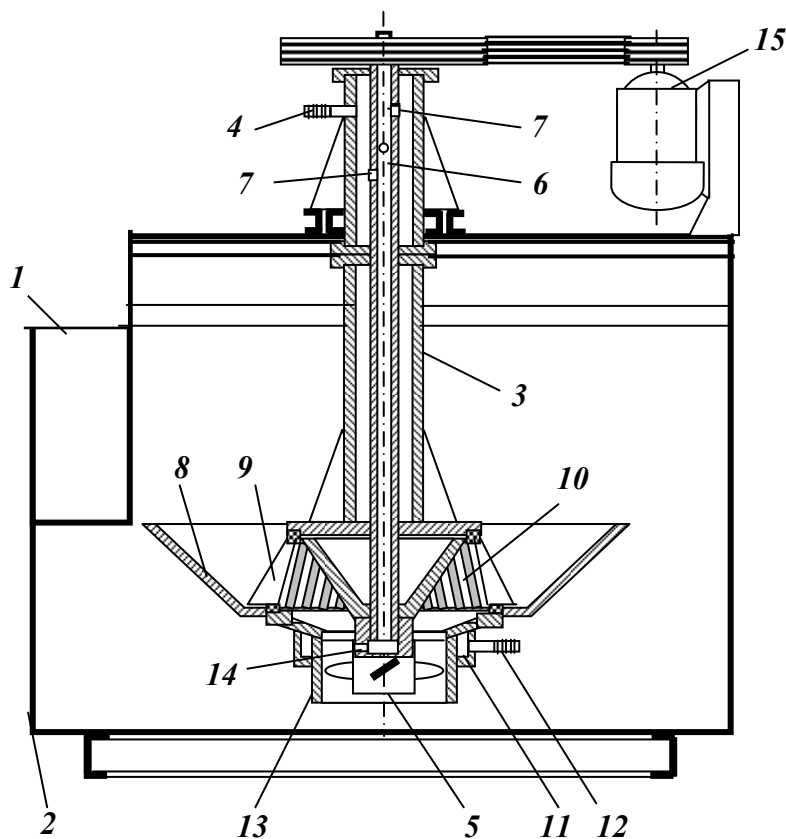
Схема пневмомеханічної флотаційної машини типу ФПМУ-6,3.
